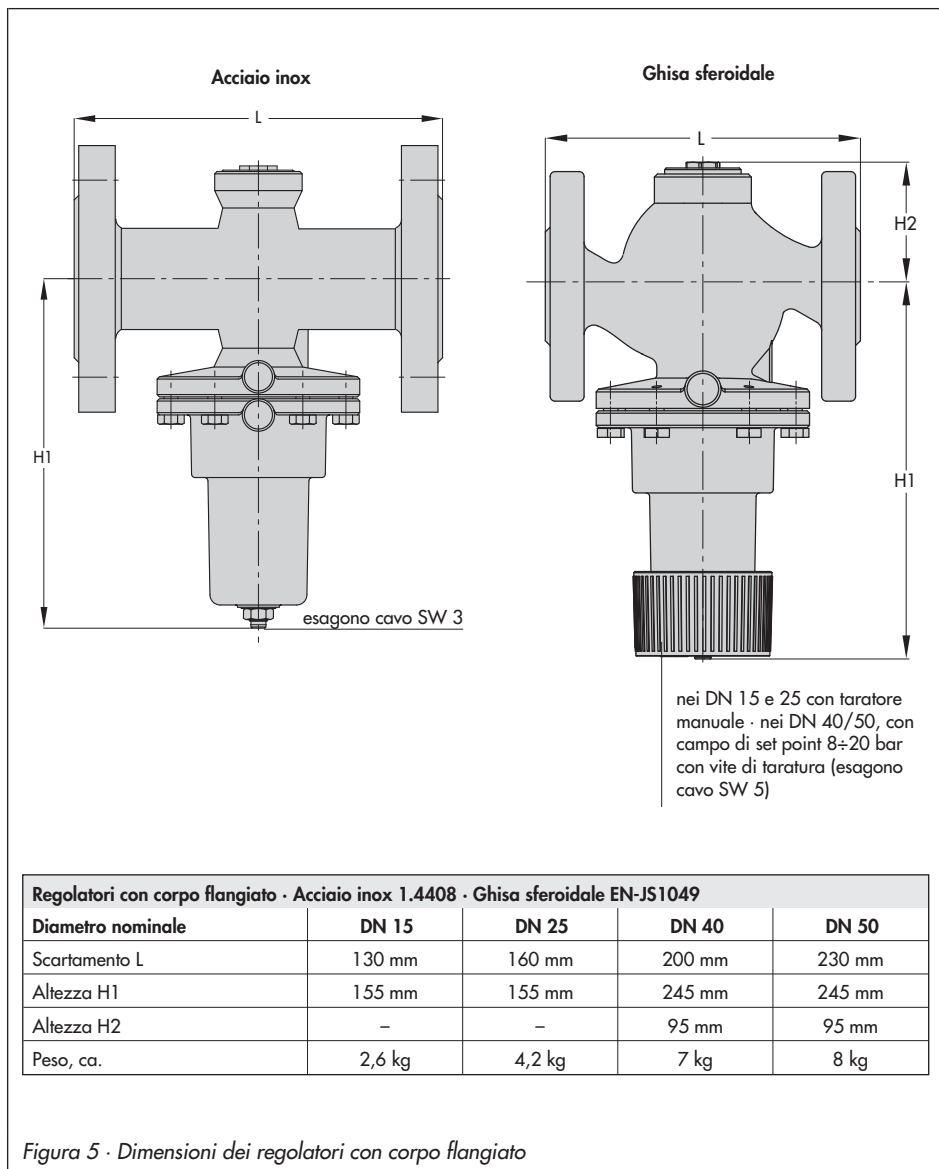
· Dimensioni dei regolatori con corpo flangiato
